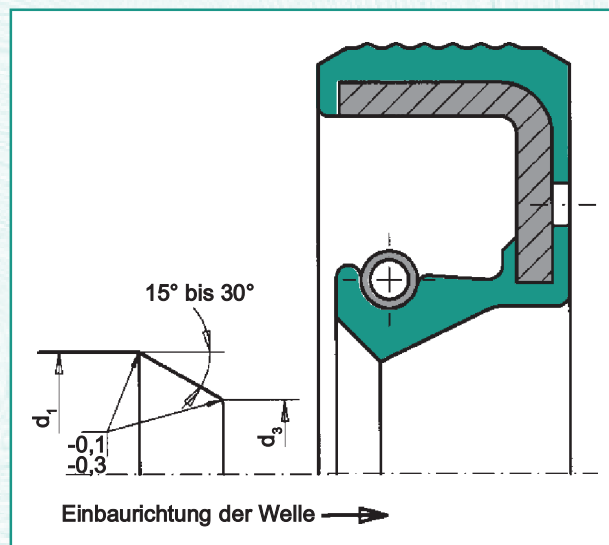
Wellenanfassung bei Einbaurichtung gegen die Stirnfläche des RADIA®-Wellendichtringes
